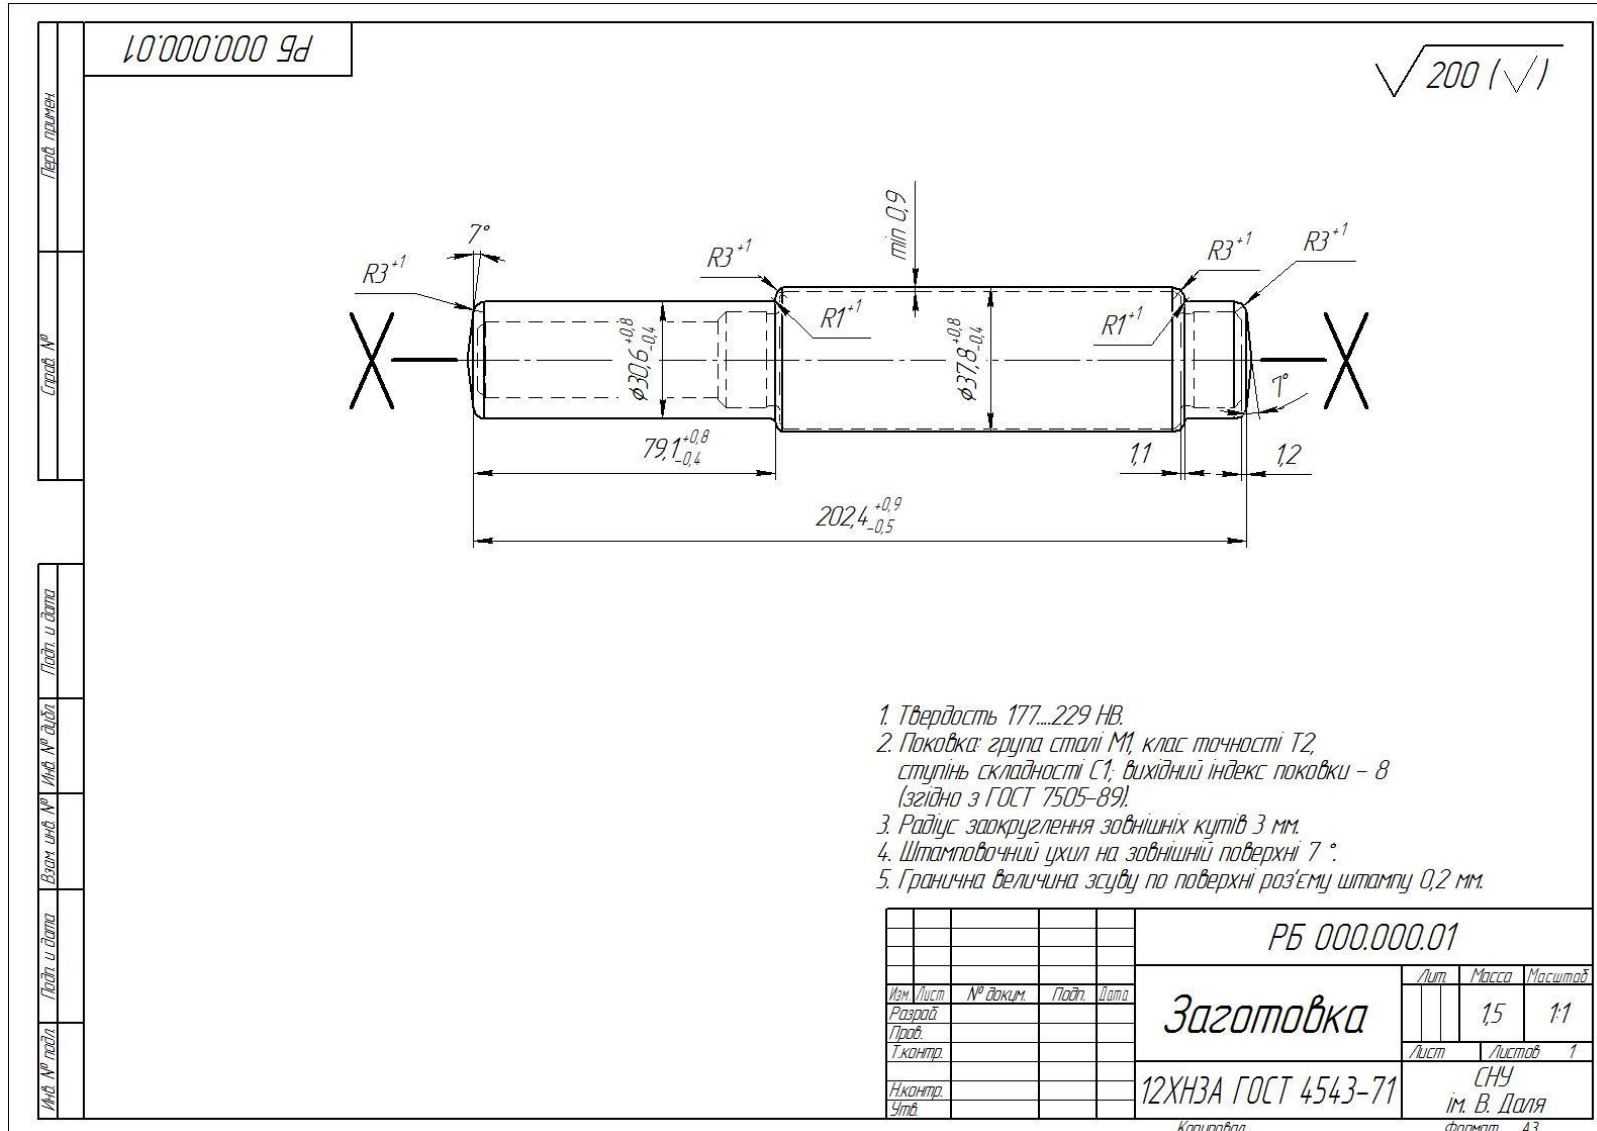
Приклад кресленика заготовки деталі «Вал шліцьовий»
